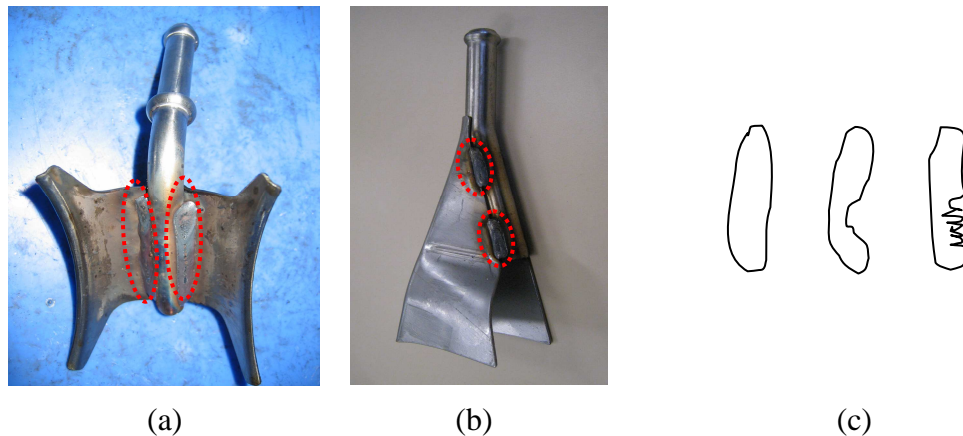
Exemple de deux types de pièces soudées (Type 1 – (a), et Type 2 – (b)). Ces deux pièces sont de bonne qualité. (c) Trois représentations schématiques de soudures. De gauche à droite, ces soudures sont respectivement bonne, trop fine et pour la dernière fine et discontinue.
